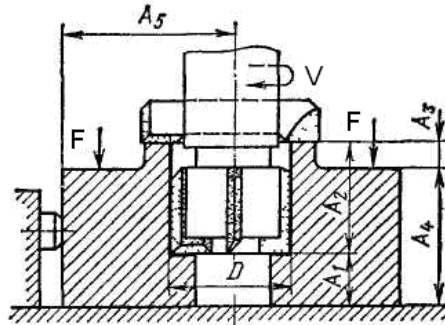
Схема обробки поверхонь заготовки (до задачі 1.17.)
